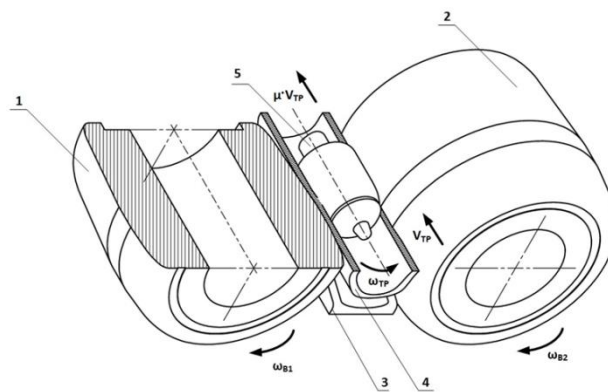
Схема процесса обкатки: 1, 2 – валки обкатного стана; 3 – направляющая проводка; 4 – труба; 5 – оправка
